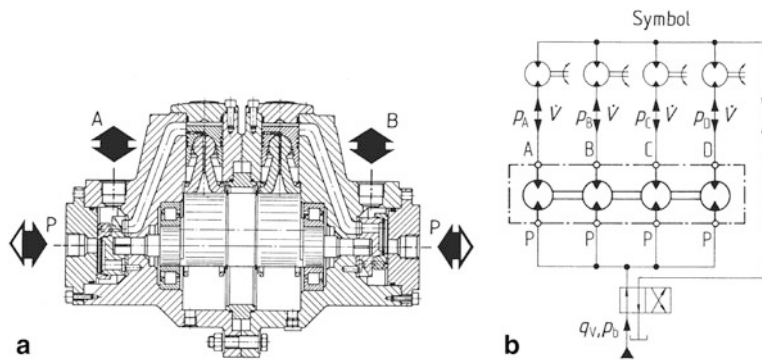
Stromteiler nach Verdrängerprinzip. a Aufbau eines Radialkolben-Stromteilers (MTw, Jahns [99]); b Gleichlaufschaltung mit Mehrstromteiler durch mechanisch gekoppelte Motoren
